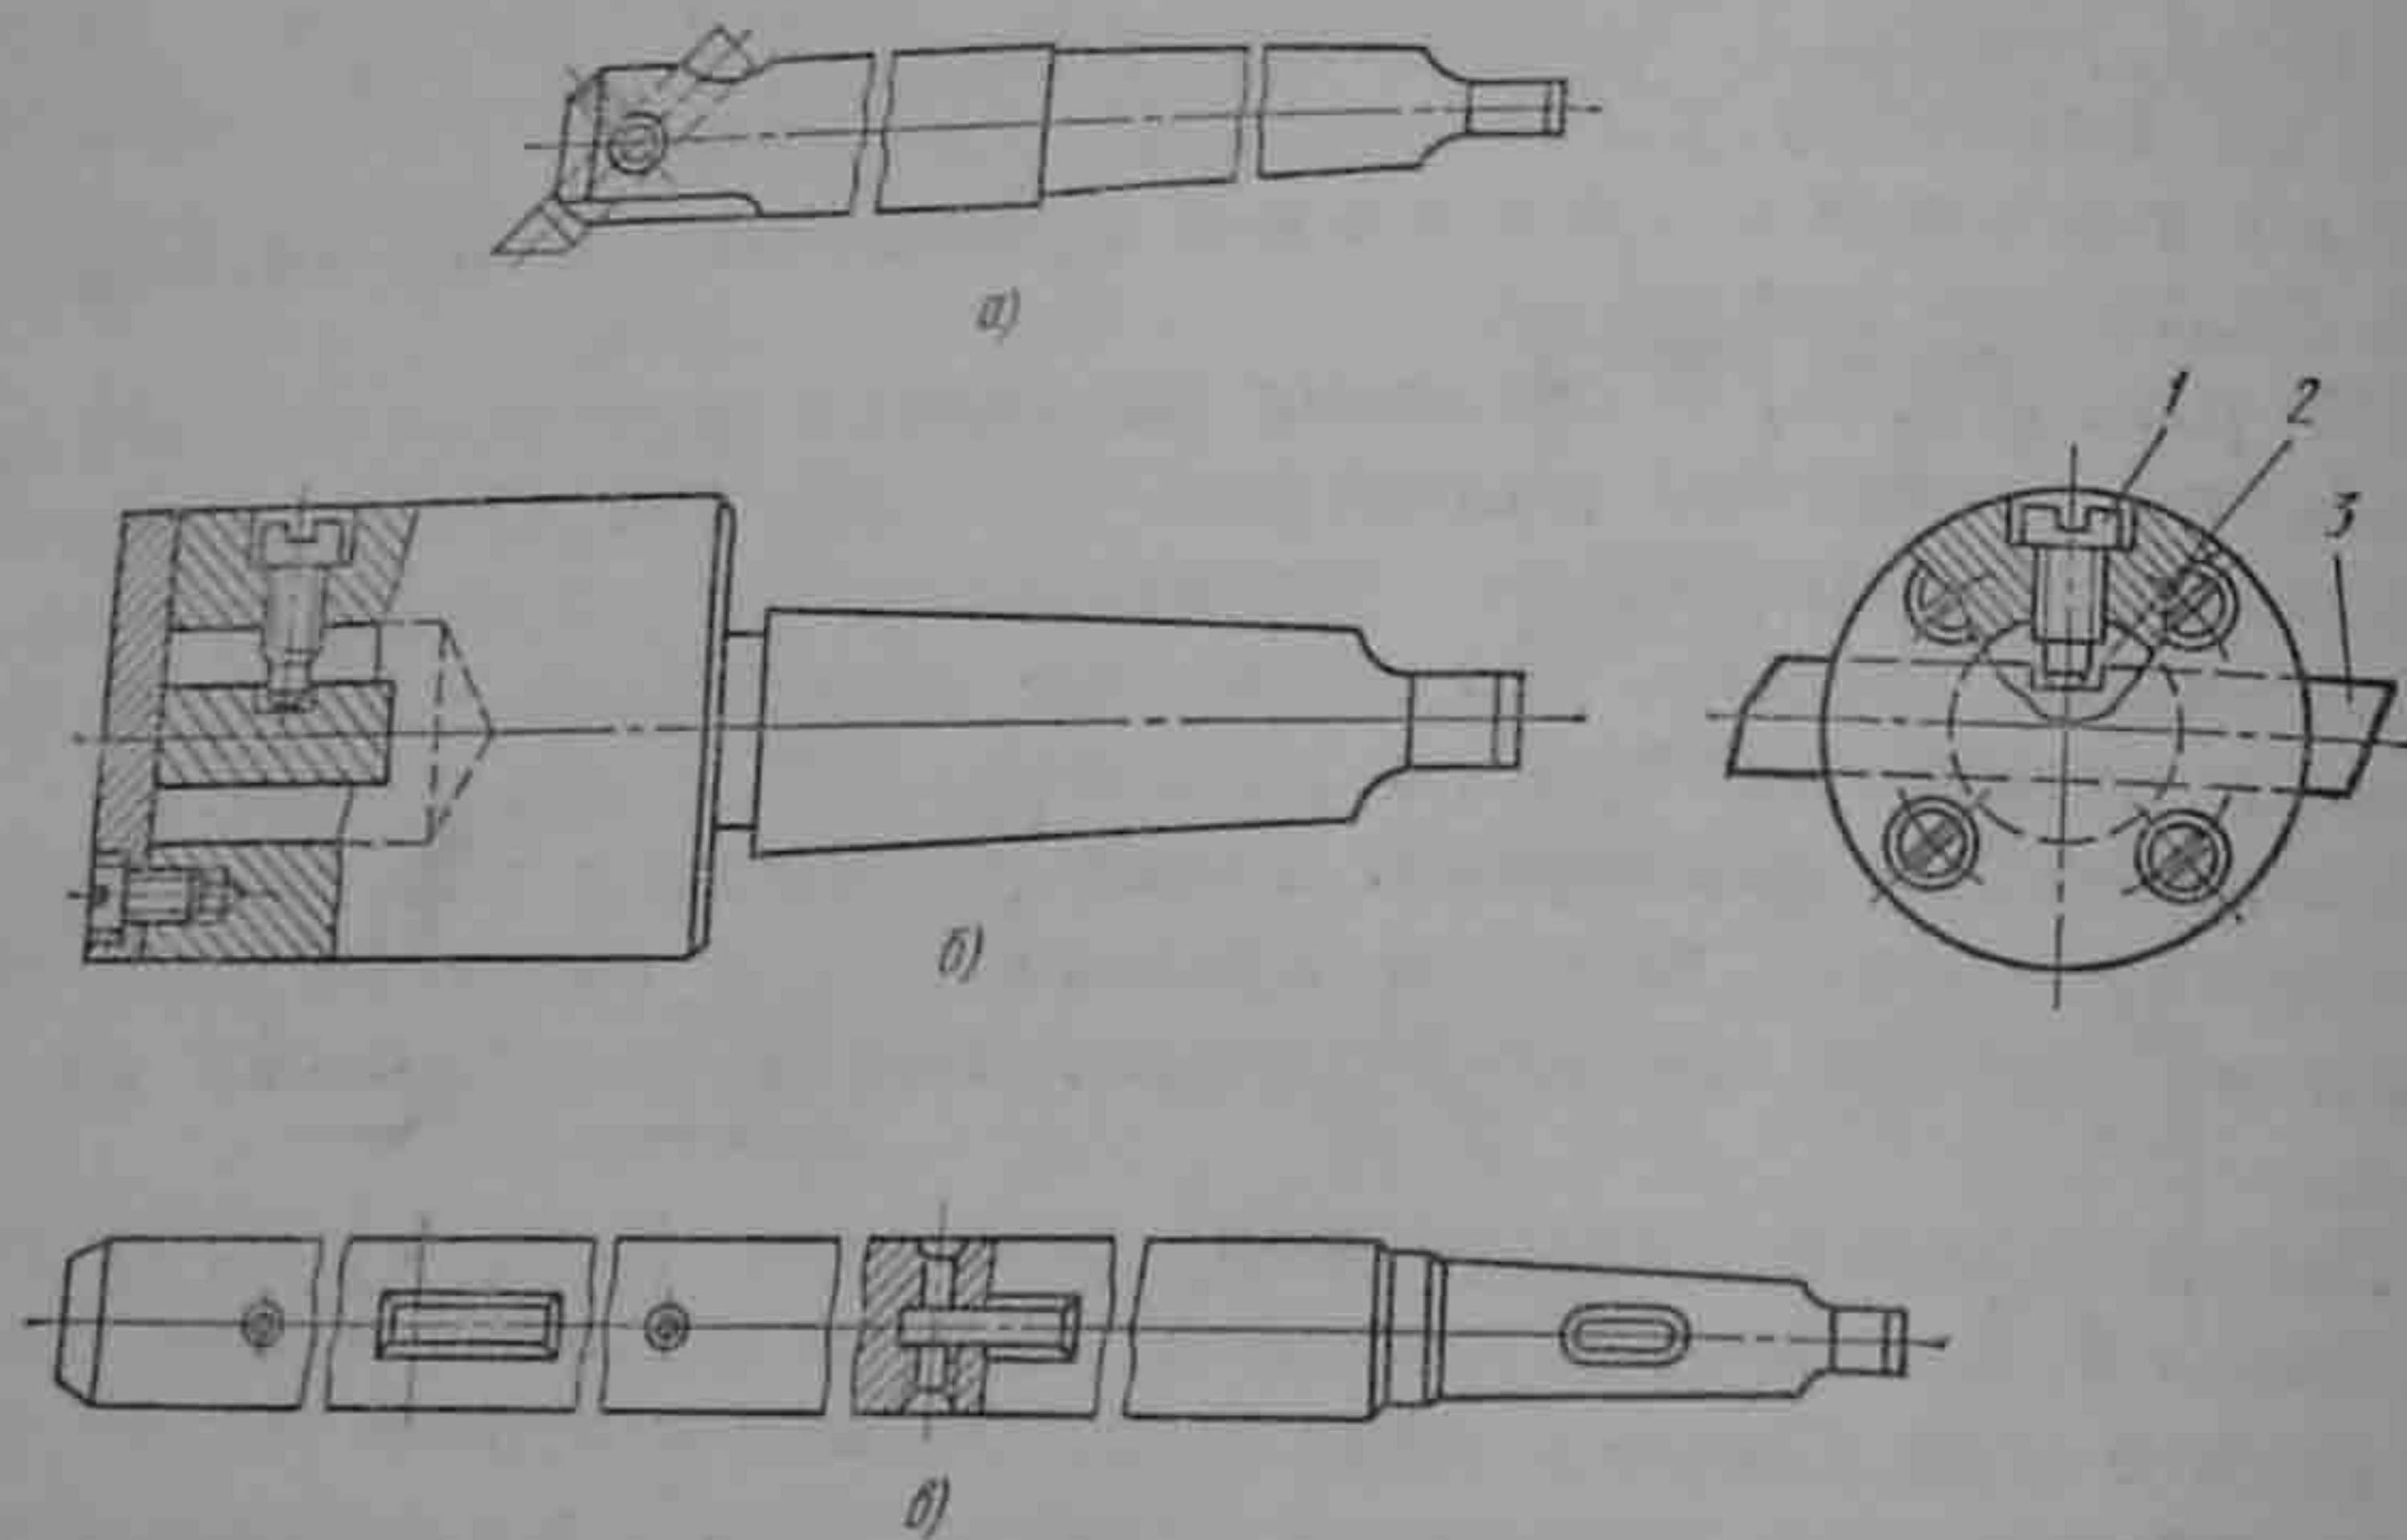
Оправки для закрепления режущего инструмента на расточных станках
